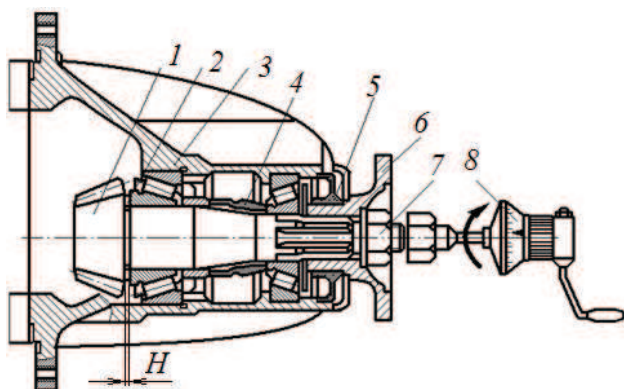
Схема проверки момента проворачивания ведущего колеса (без дифференциала): *1* – ведущее колесо; *2* – регулировочное кольцо; *3* – корпус; *4* – распорная втулка; *5* – сальник; *6* – фланец; *7* – гайка; *8* – динамометр; H – толщина регулировочной прокладки
